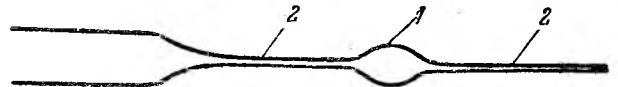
Заготовка пулек: 1 — пулька; 2 — ус
